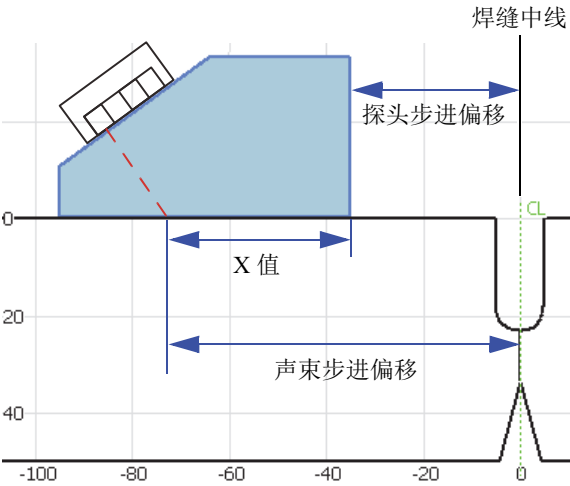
焊缝检测中声束步进偏移的示例
